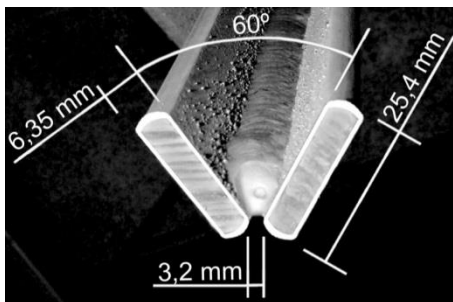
Dimensões do corpo de prova utilizado na soldagem com o TARTÍLOPE V2F.
